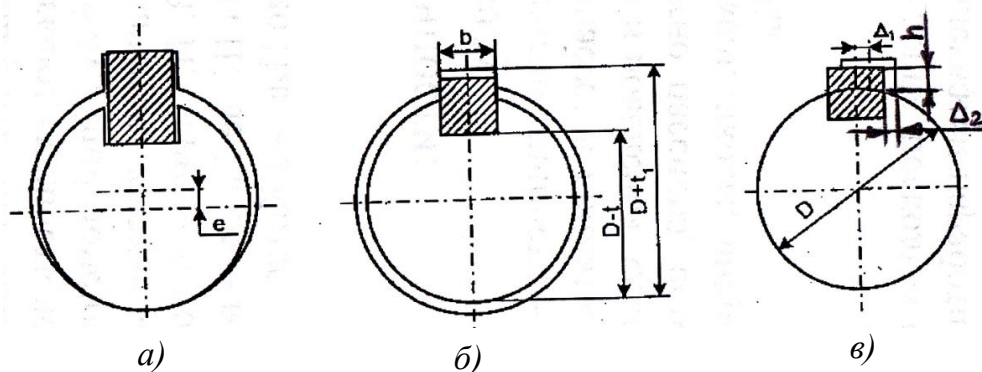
Смещение деталей шпоночного соединения при сборке
